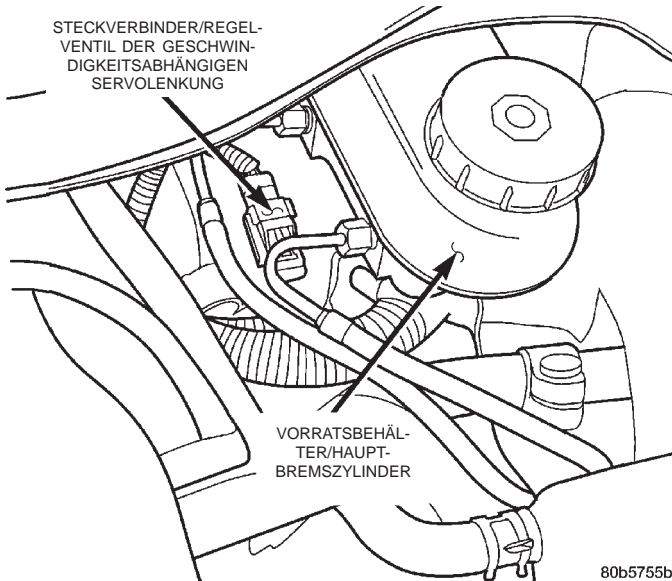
Kabelbaum-Steckverbinder für Regelventil der Servolenkung
